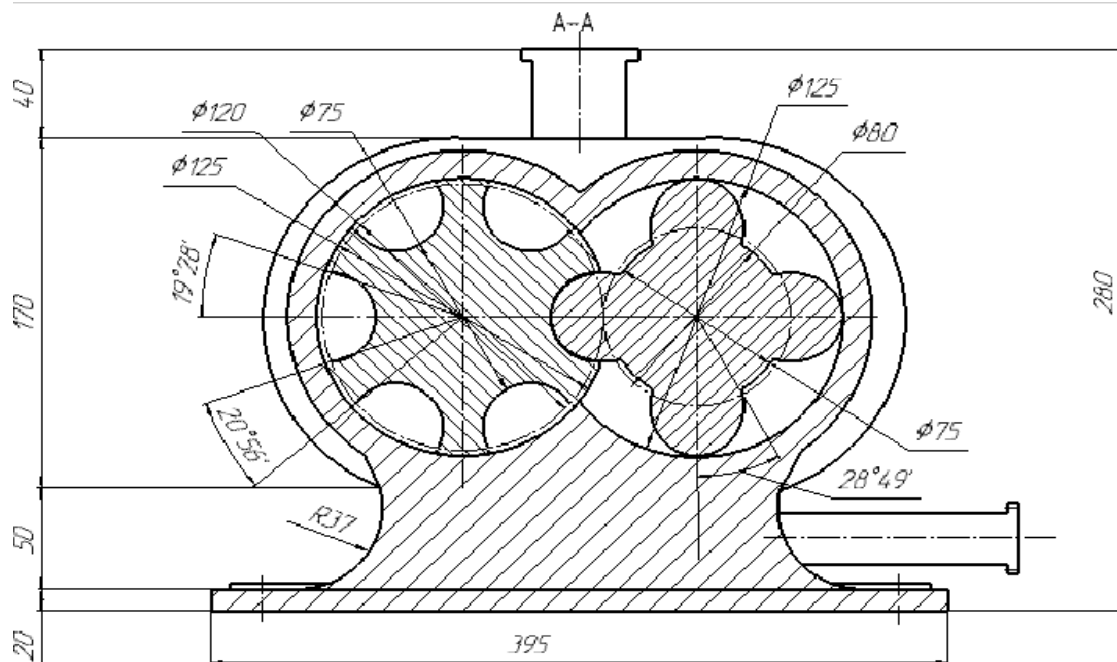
Поперечний розріз гвинтового компресора 1 ступеня
